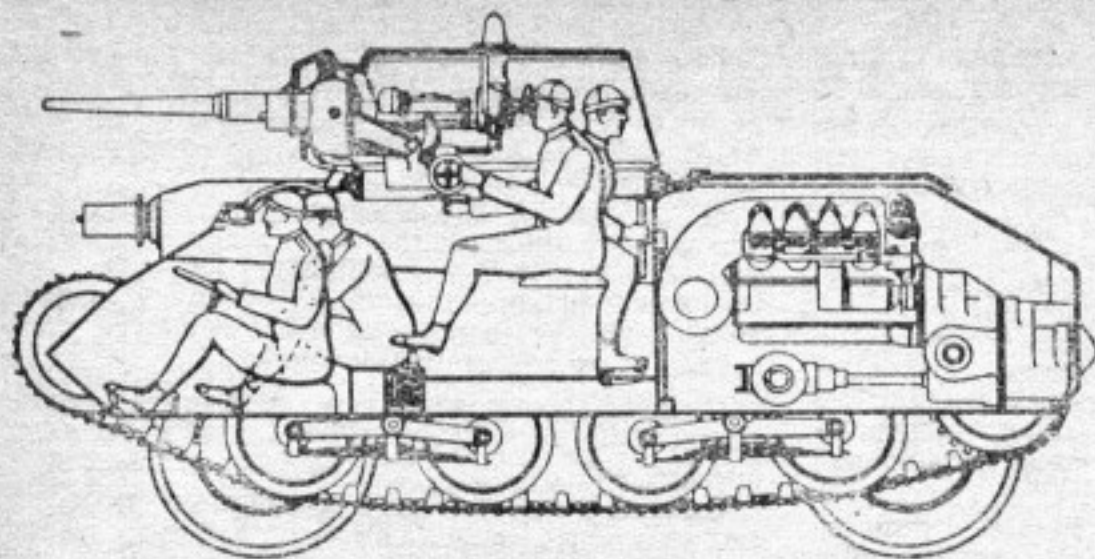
Разрез шведского колесно-гусеничного танка «Ландсверк-30».
